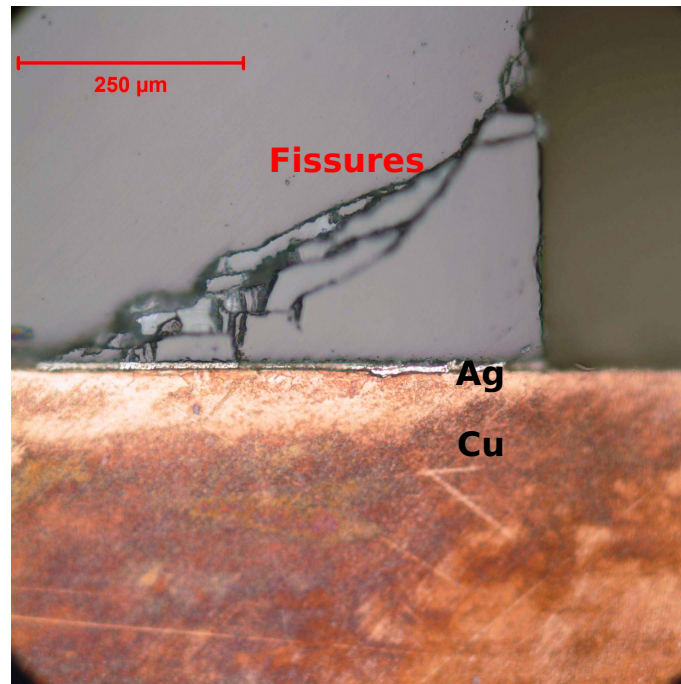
Image optique du joint de l'assemblage Q. On remarque que la puce est dégradée.
